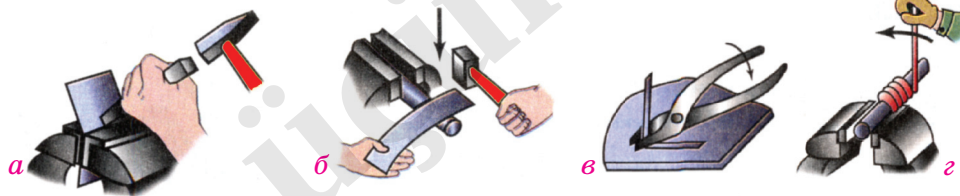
Сгибание заготовки: а – в тисках; б – на оправке; в – круглогубцами; г – в гибочном приспособлении
